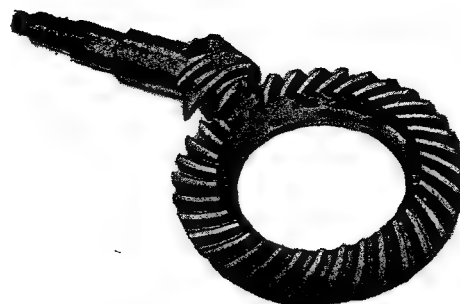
Juego de engranajes cónicos con dentado hipóide.
